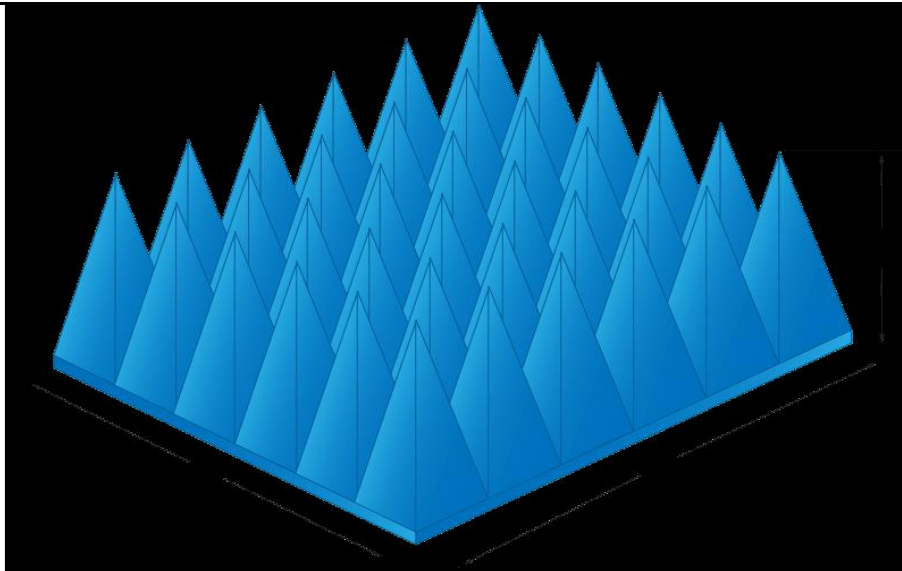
Dessin technique de l'absorbeur pyramidal de forme carrée [1]
